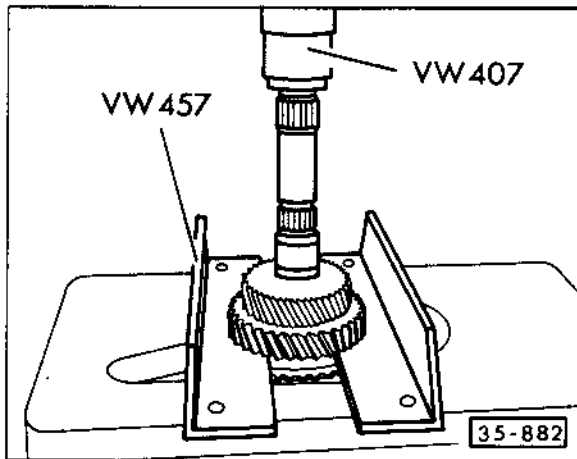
Zahnrad für 3. Gang mit Schaltrad für 2. Gang abpressen
